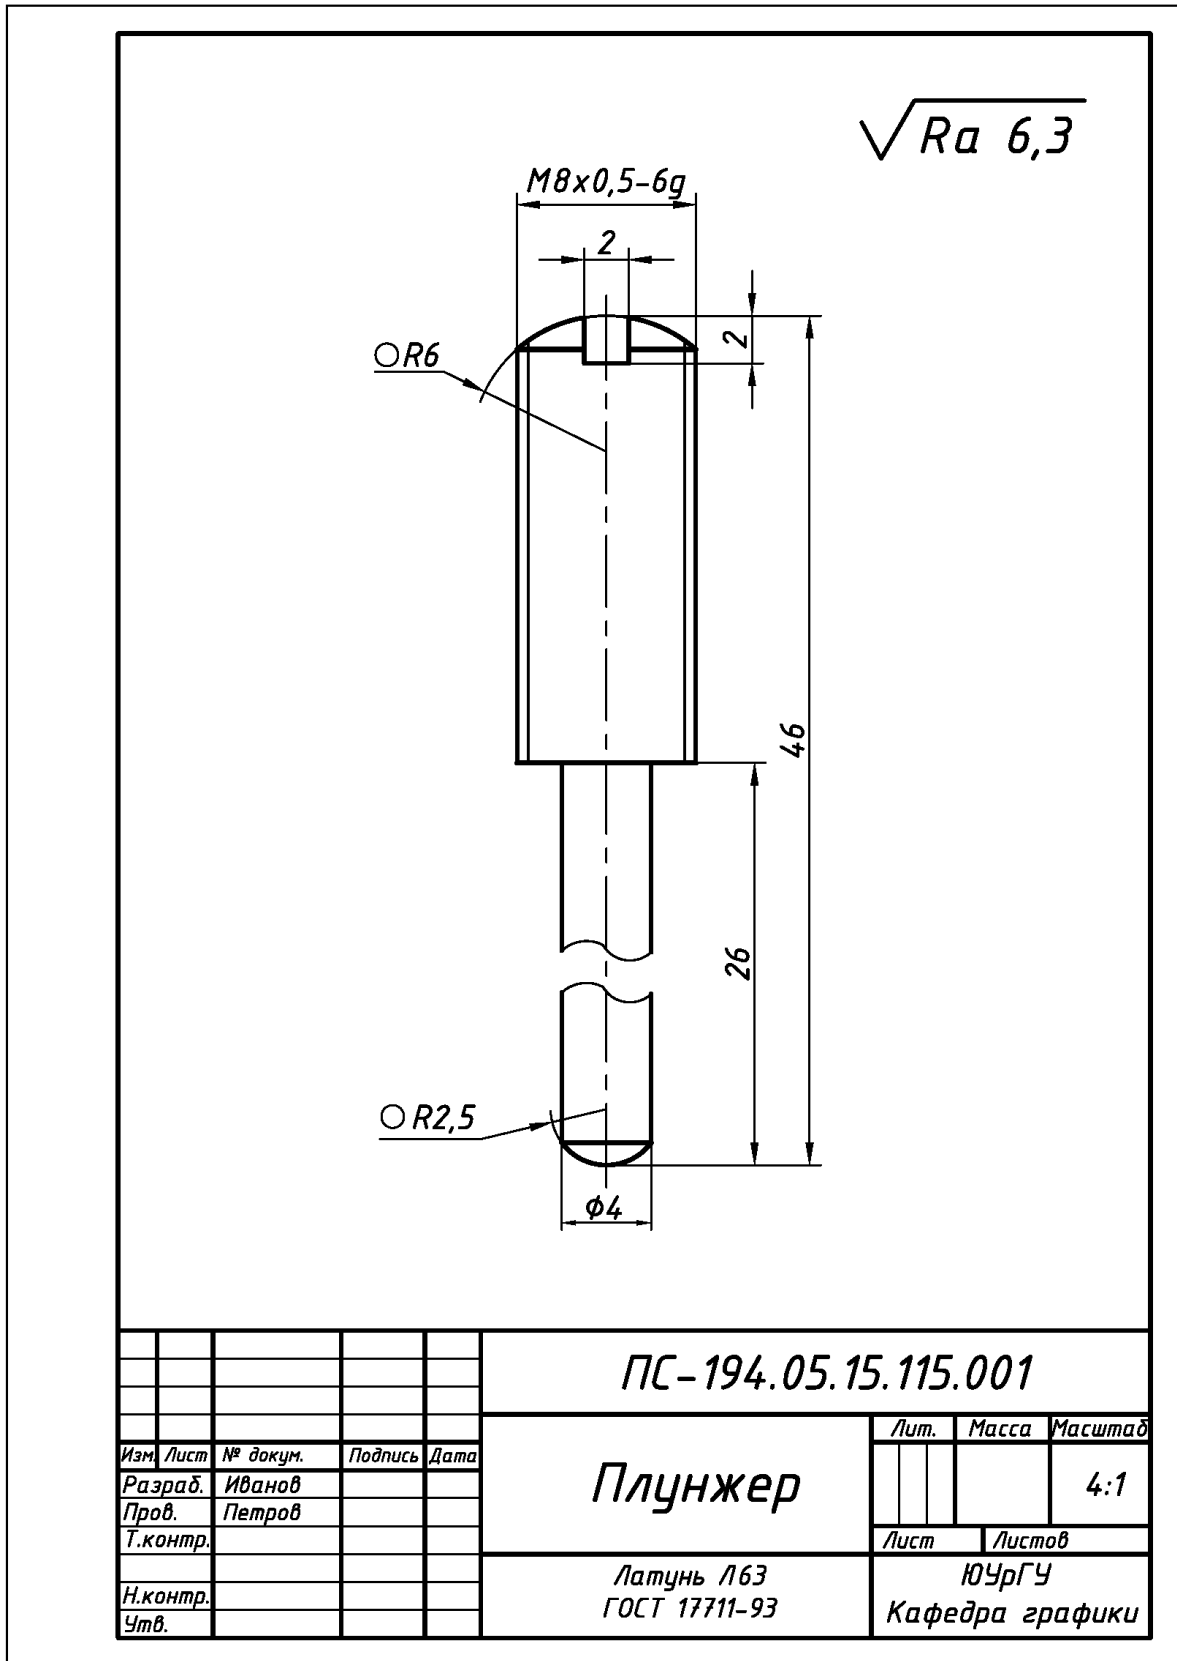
Пример выполнения и оформления рабочего чертежа детали «Плунжер» (поз. 3), входящей в состав чертежа общего вида изделия «Резонатор» (см. рис. 8.1)
